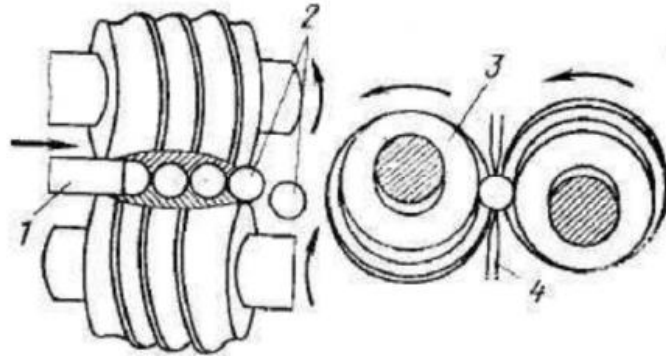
Схема поперечно-гвинтової прокатки куль: 1 - заготовка; 2 – готові вироби; 3 - робочі валки з гвинтовими калібрами; 4 – проводки
